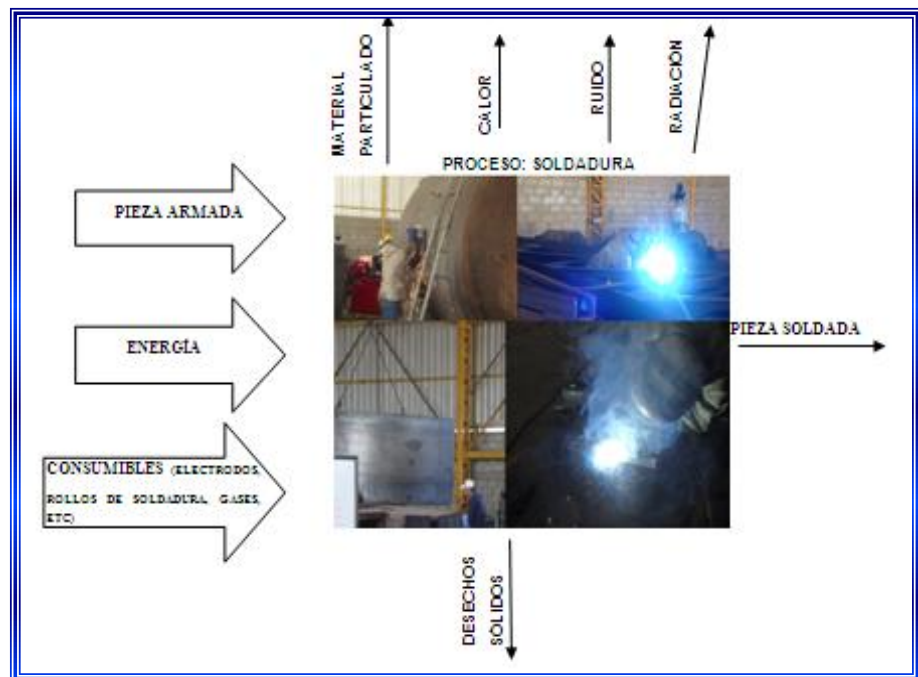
CAJA DE PROCESO DE SOLDADURA.
